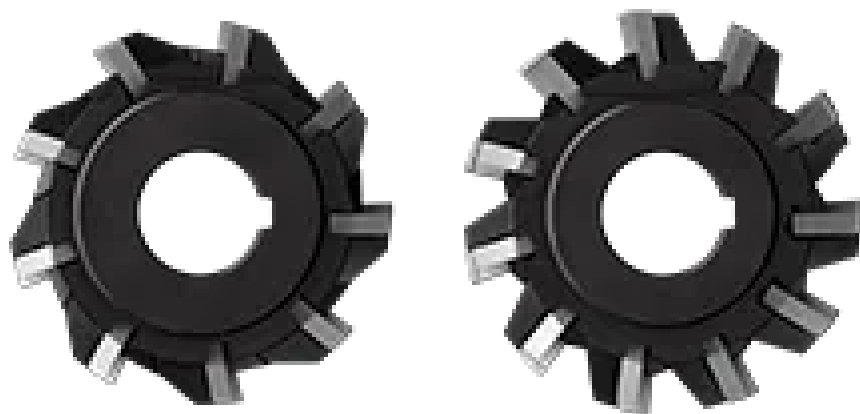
Фреза CoroMill 176-080A32-2.5
